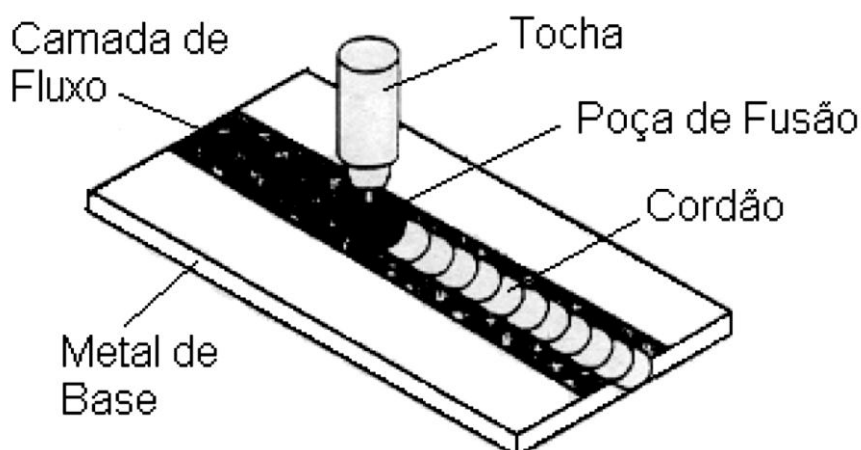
Soldagem ATIG <sup>[4]</sup>.
